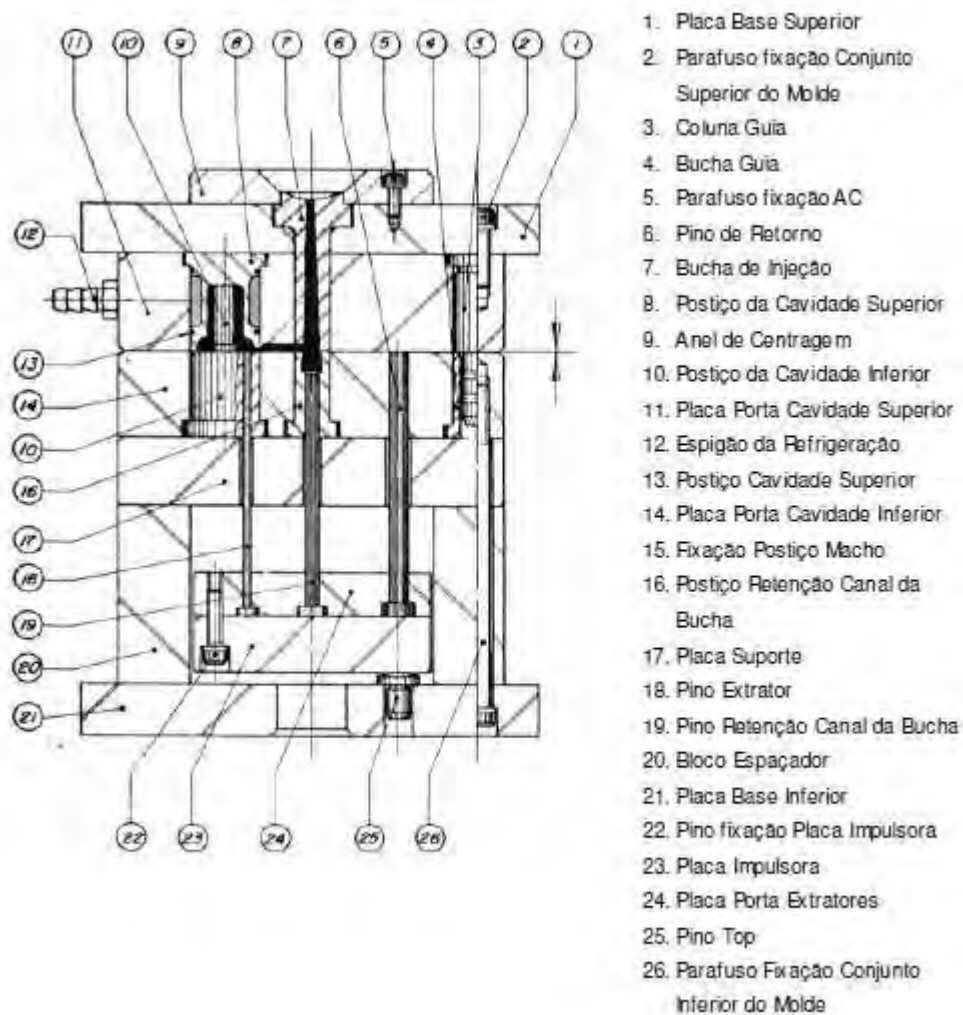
Exemplo de molde de duas placas e seus componentes (MANRICH, 2005)
